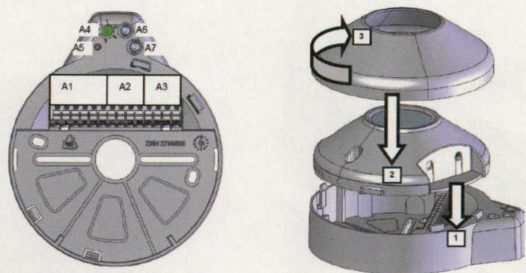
Przykładowa konstrukcja czujnika ruchu
